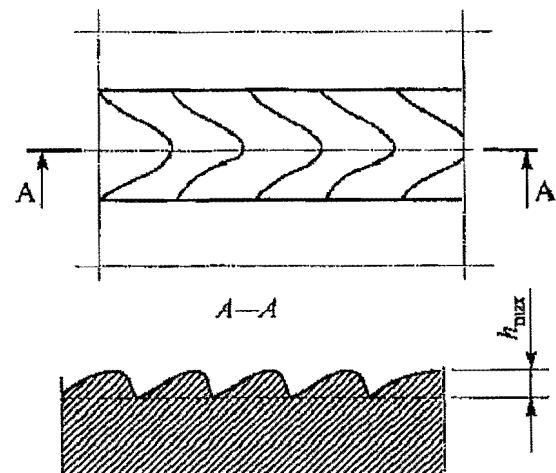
35. Чешуйчатость сварного шва
